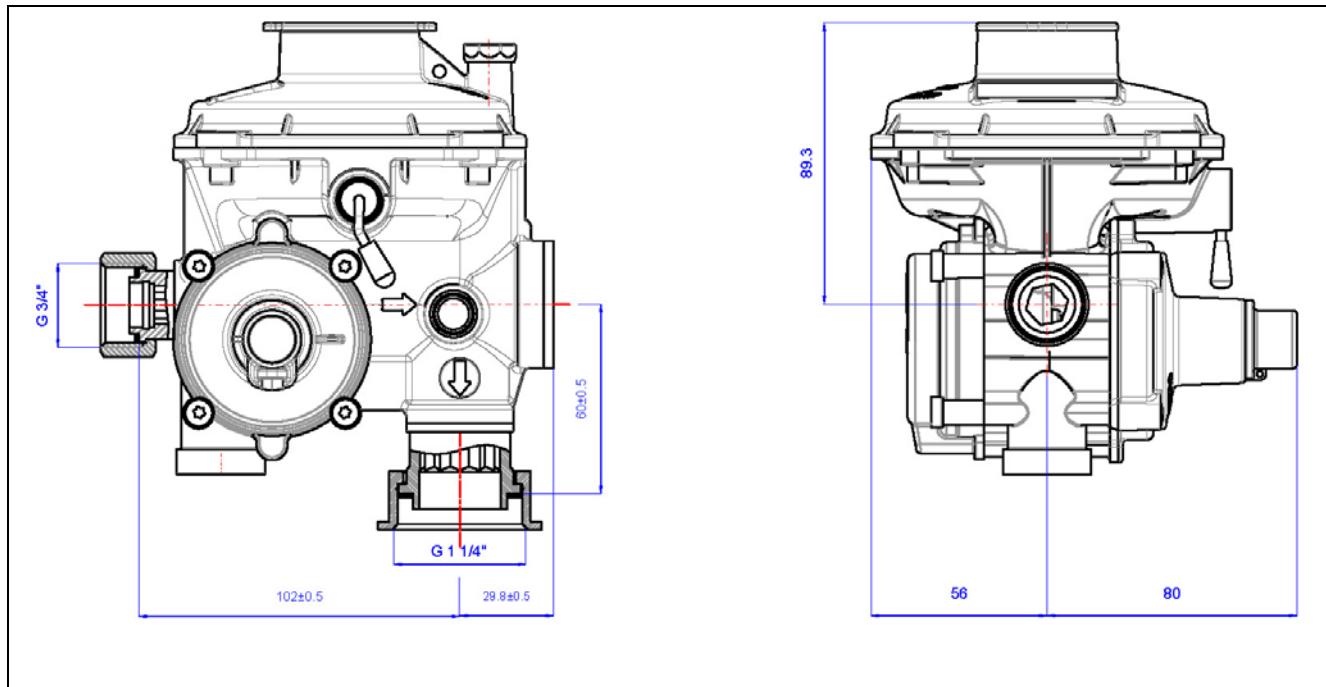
Габаритные и присоединительные размеры регулятора давления РД с угловым присоединением к трубопроводу
